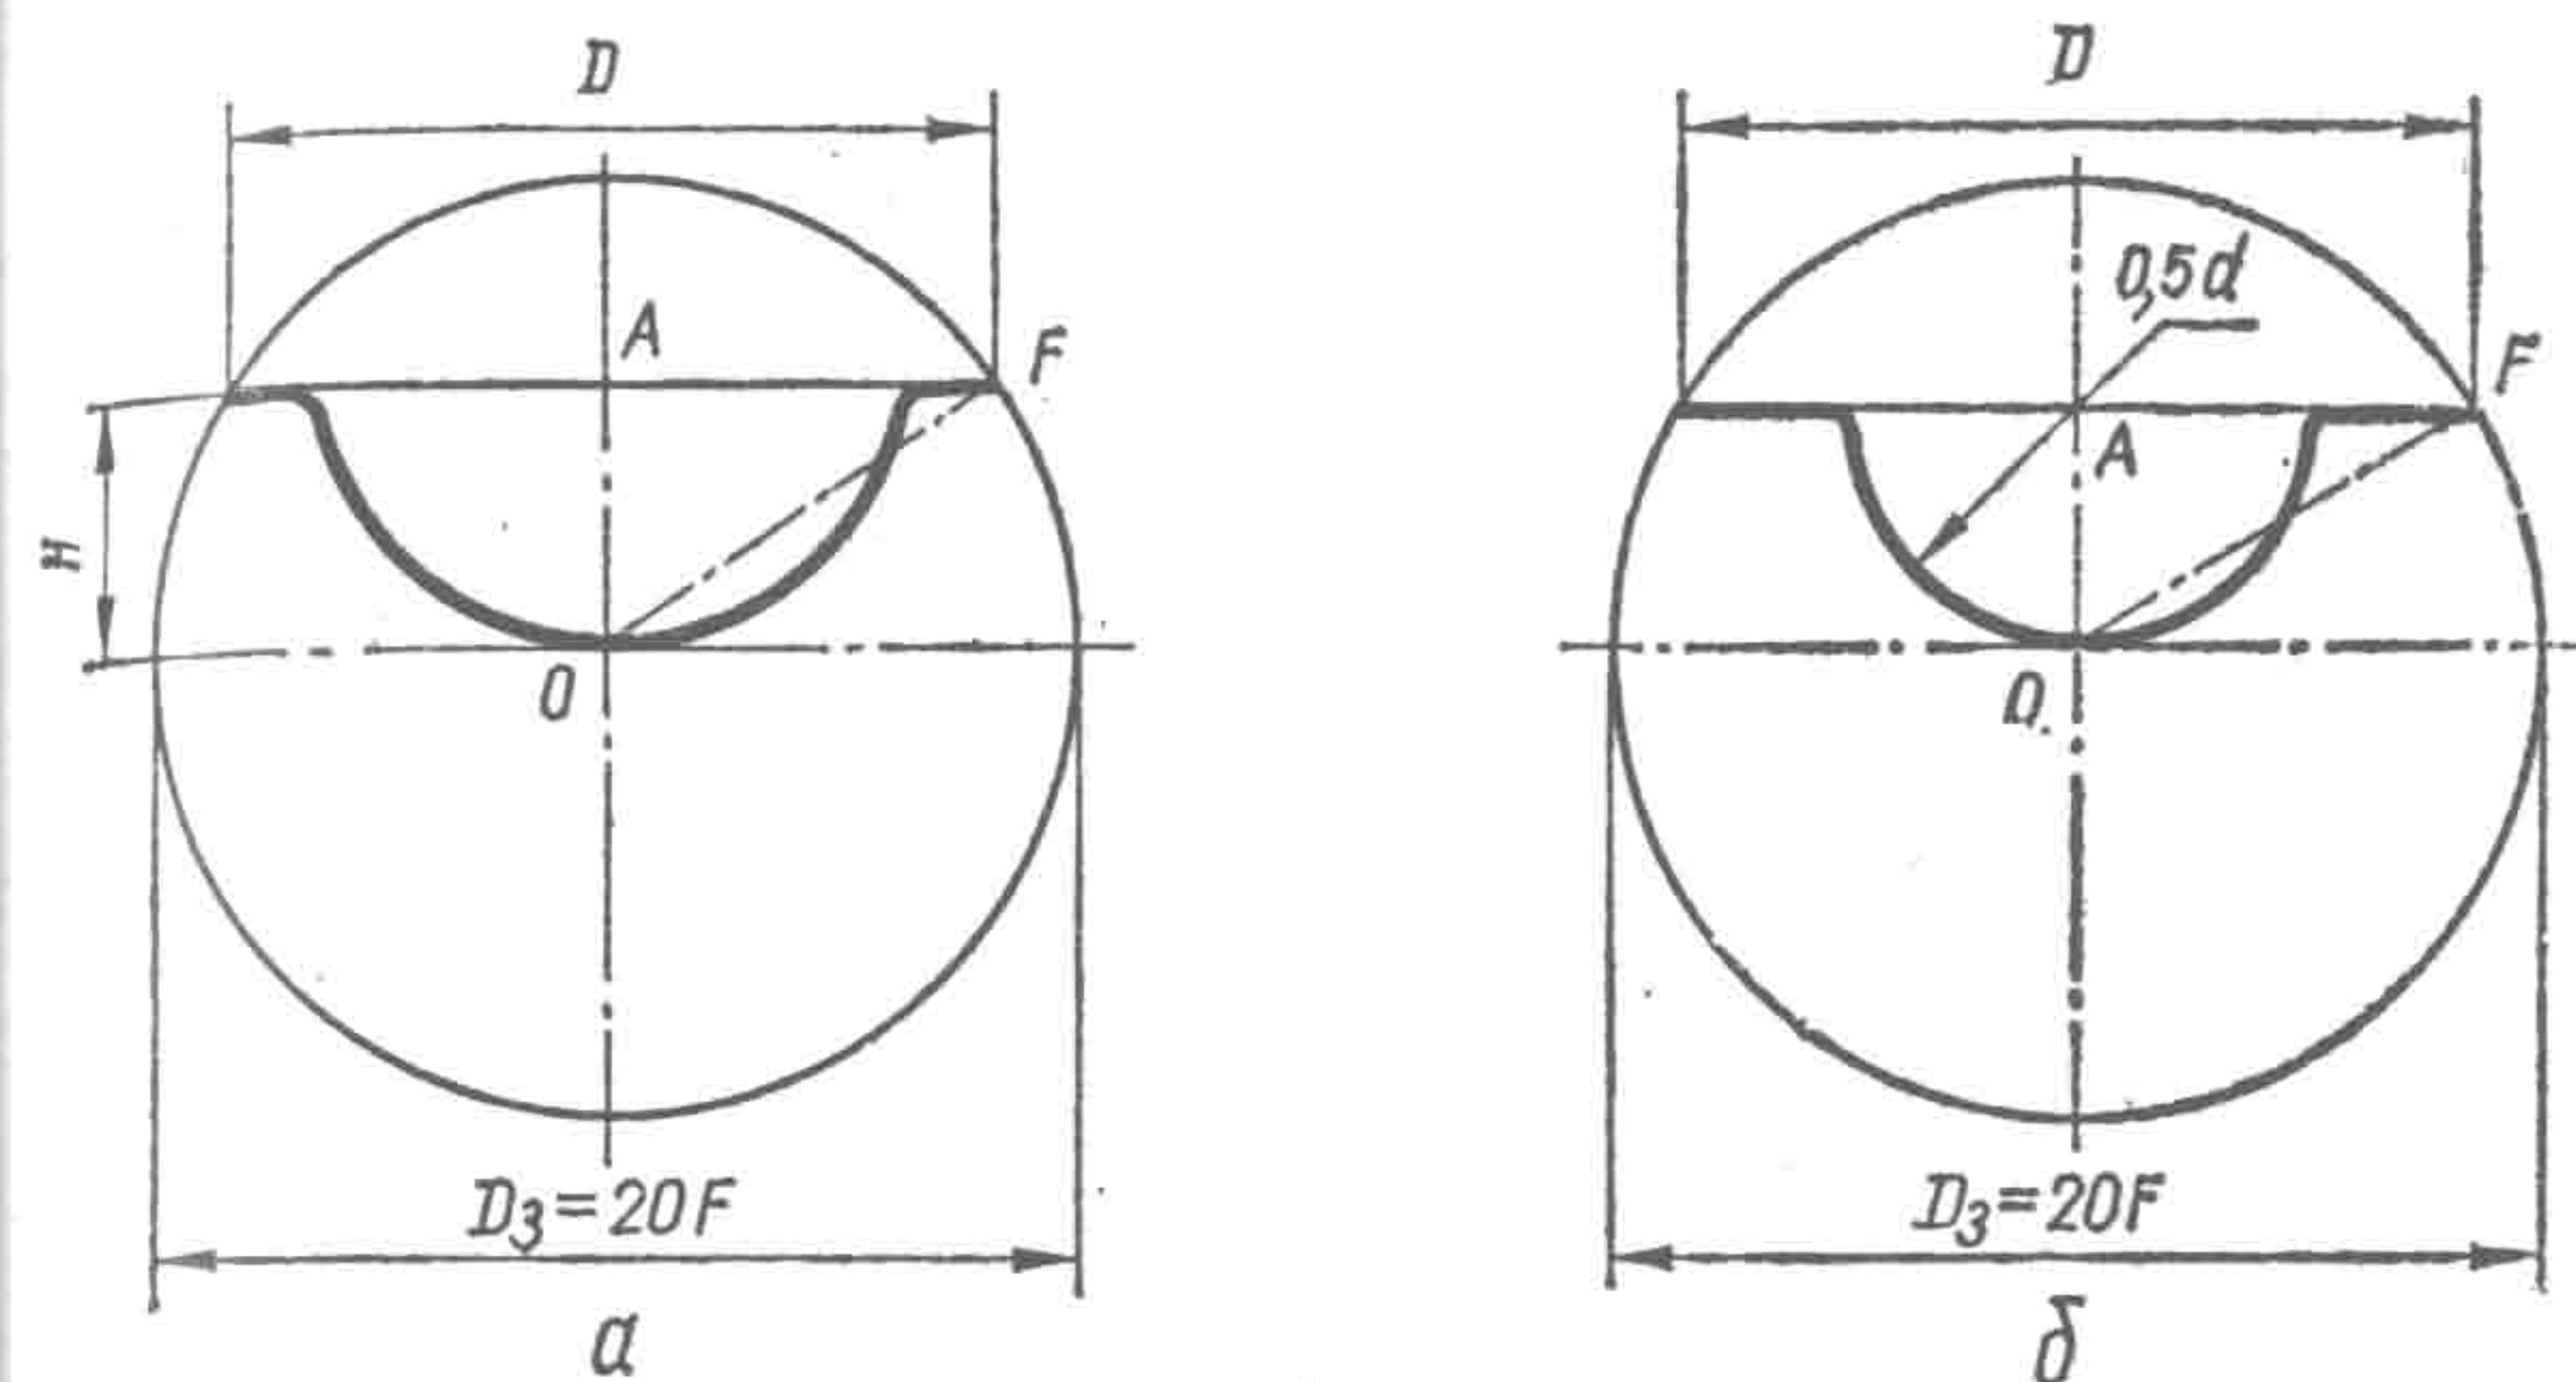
Определение размеров заготовки графическим методом: а — сегмента с фланцем; б — полушария с фланцем.
